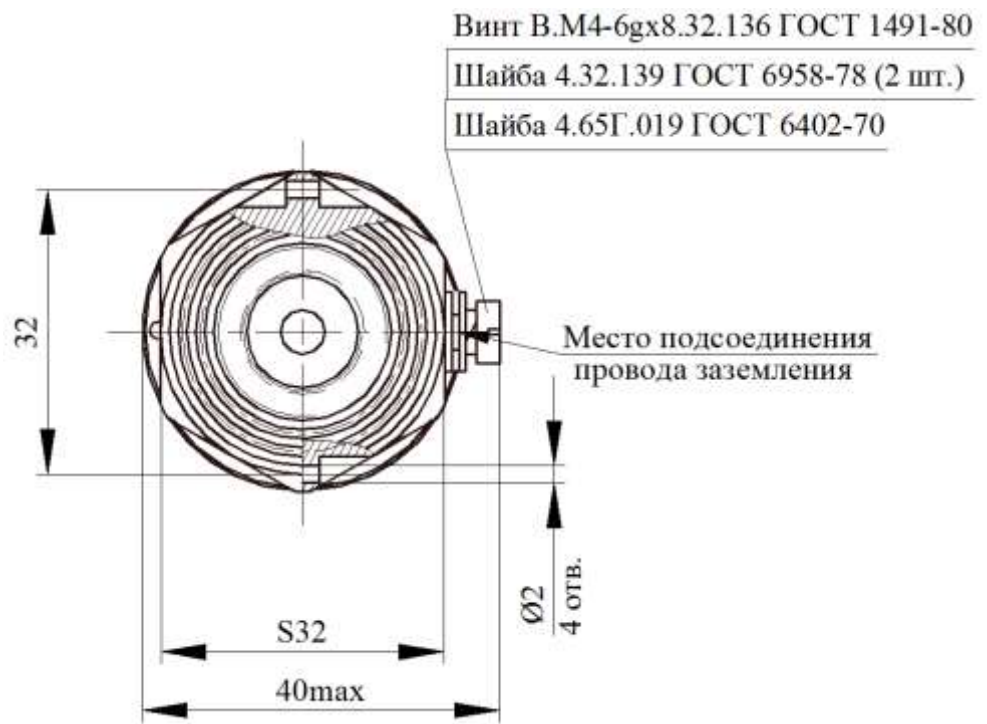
Вид на соединитель электрический СДВ и гайку корпуса.
